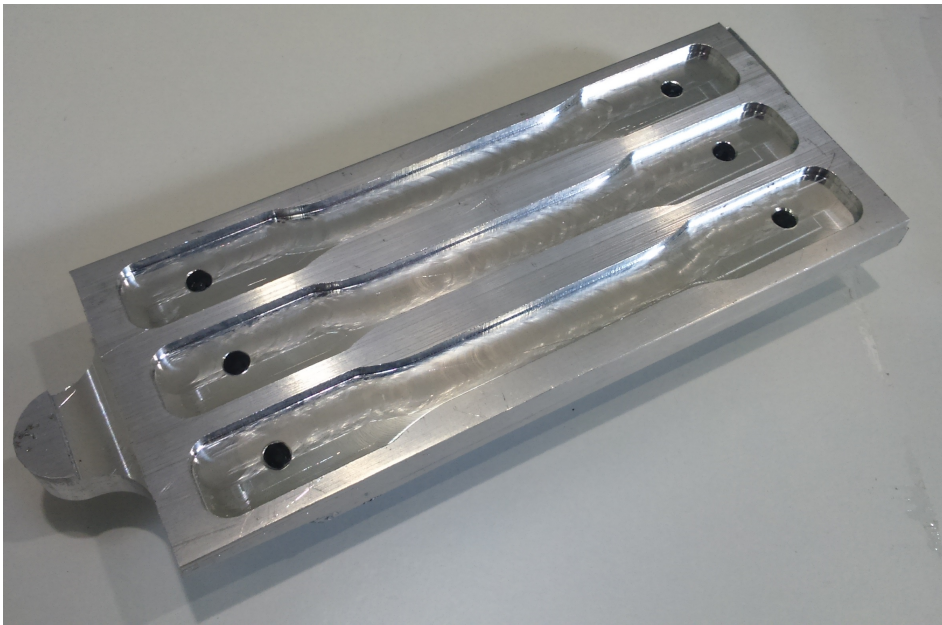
Molde mecanizado para fabricar probetas de resina.
